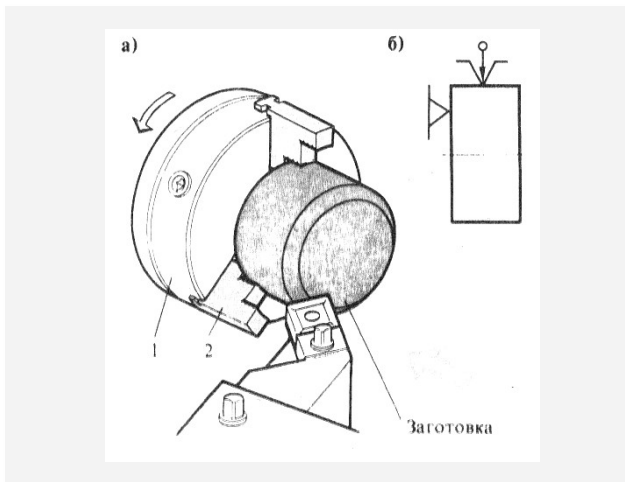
Установка заготовки в патроне (а), условная схема (б). Технологические базы – торец и ось заготовки.
